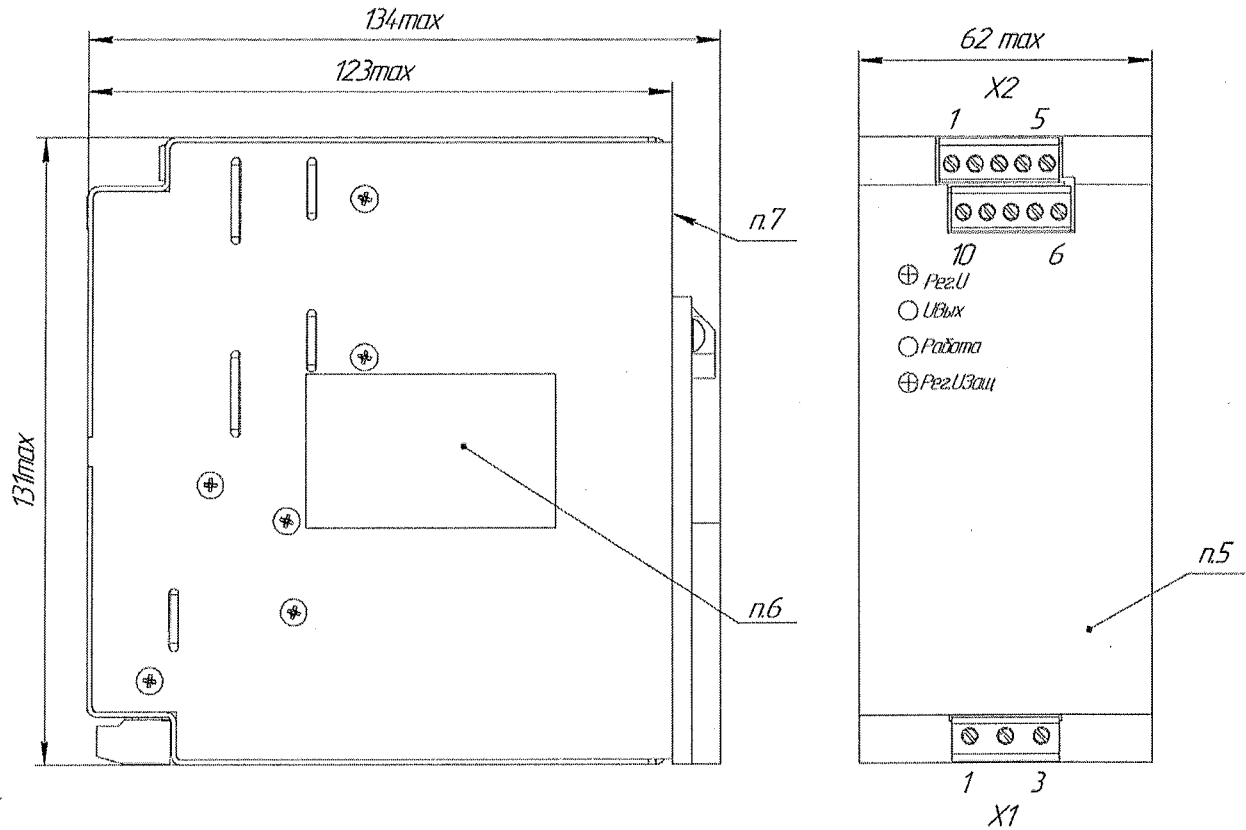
Габаритные размеры модуля КАН-Д500
